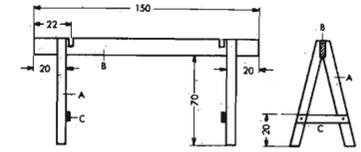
Costruzione dei cavalletti. A destra, vista laterale.
